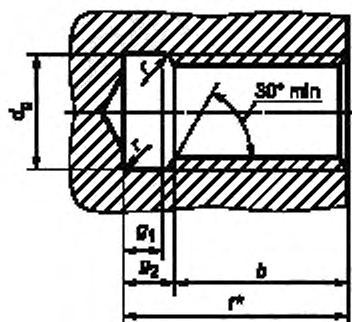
Резьбовое глухое отверстие со сбегом резьбы
